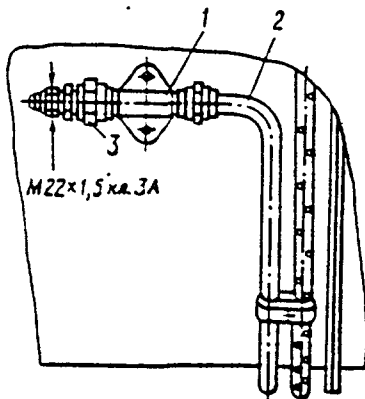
Патрубок забора воздуха на заднем корпусе камеры сгорания (вид на двигатель справа):
